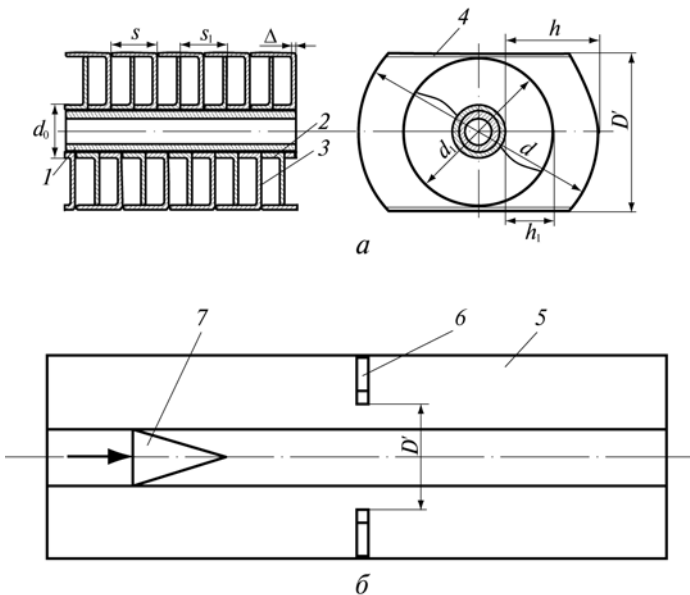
Биметаллическая труба (а) с подогнутыми KLM-ребрами и устройство (б) для подгибки ребер (вид сверху)
